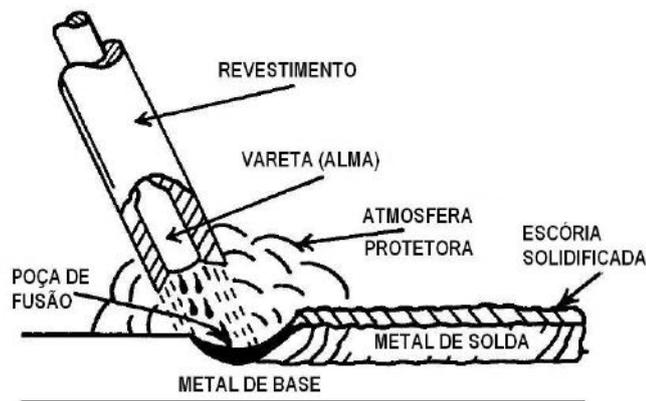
Processo de soldagem arco elétrico com eletrodo revestido
